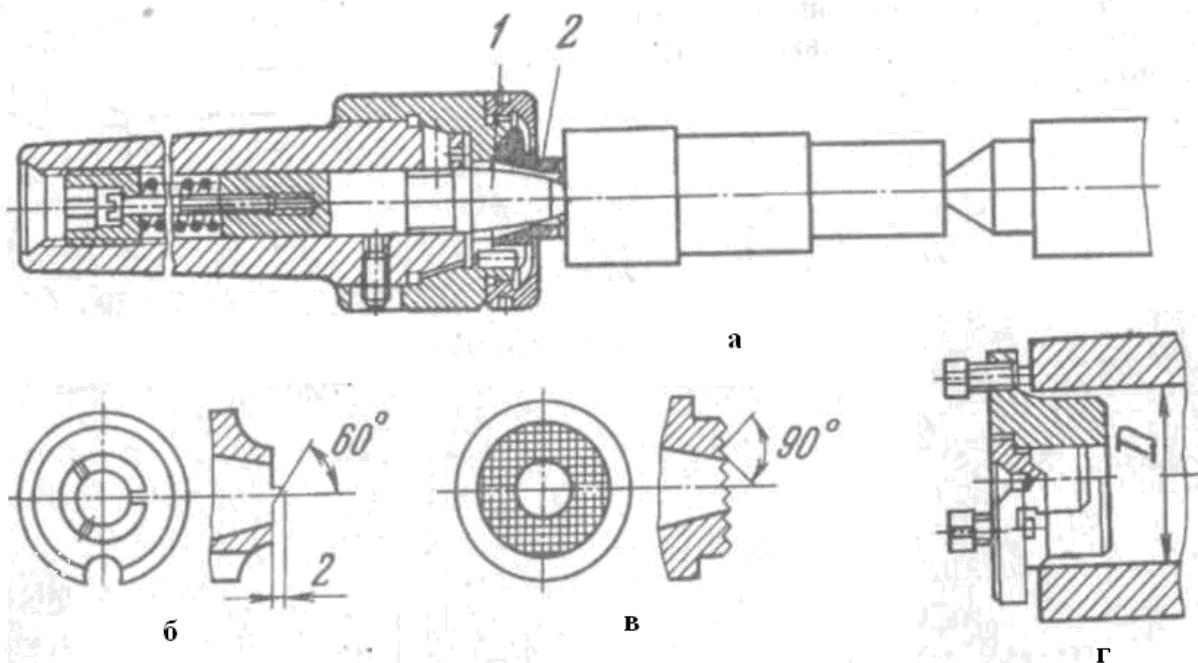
Установка заготовки в плавающий центр (а), б – трехзубая поводковая шайба, в – многозубая поводковая шайба, г – переходные пробки.
